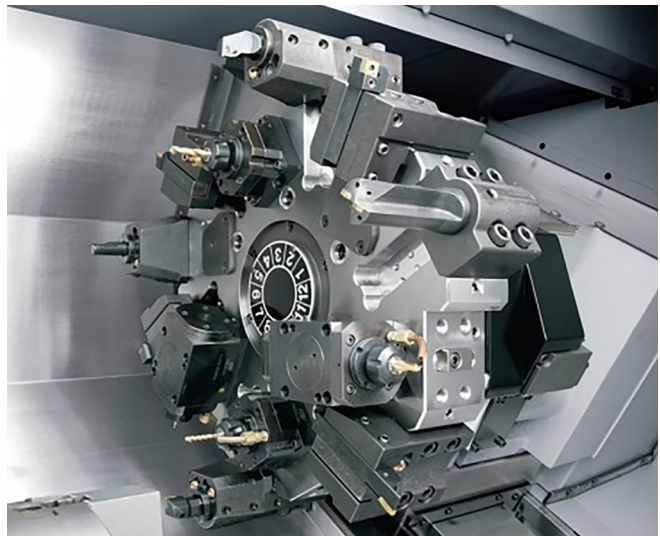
Револьверна головка токарного верстата з ЧПУ DMG MORI CL 2000 [5]
